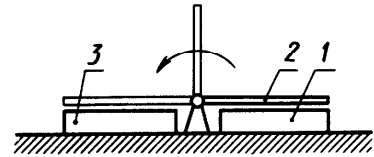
Схема устройства для сборки и сварки ферм
